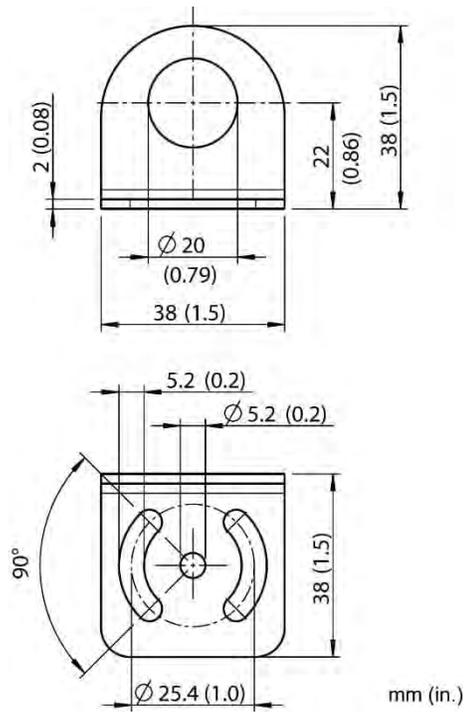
Dimensions de l'équerre de montage fixe (XXXMI3100FB)
